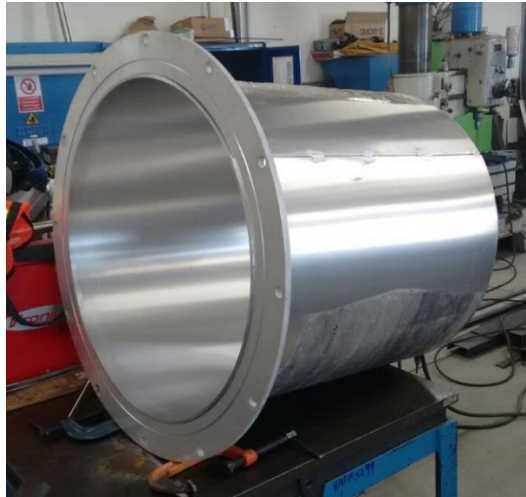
Muestra el cuerpo principal de la Boya de Monitoreo, de placa de Aluminio 6061 T6 de 1/2" para su fabricación.
